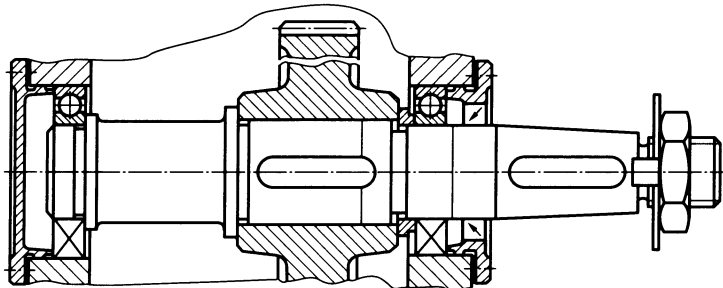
Выходной вал цилиндрического зубчатого редуктора (мотор-редуктора)
